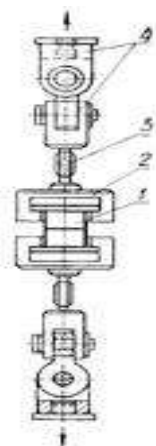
Схема приспособления для испытаний на прочность при отрыве клеевых соединений
